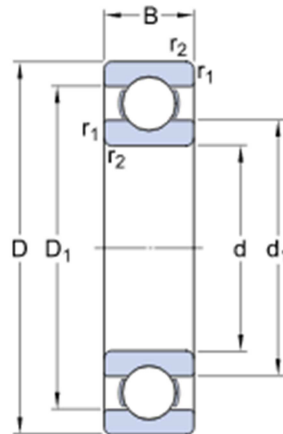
Dimensions du roulement rigide à billes 6406 de SKF
